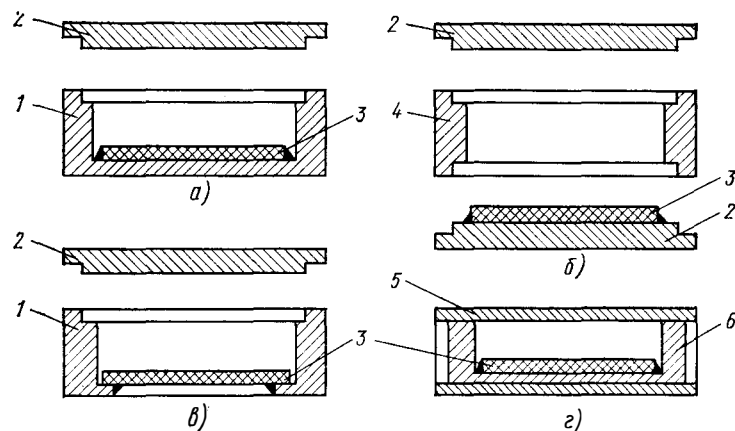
Основные типы конструкций корпусов ГИС СВЧ:
